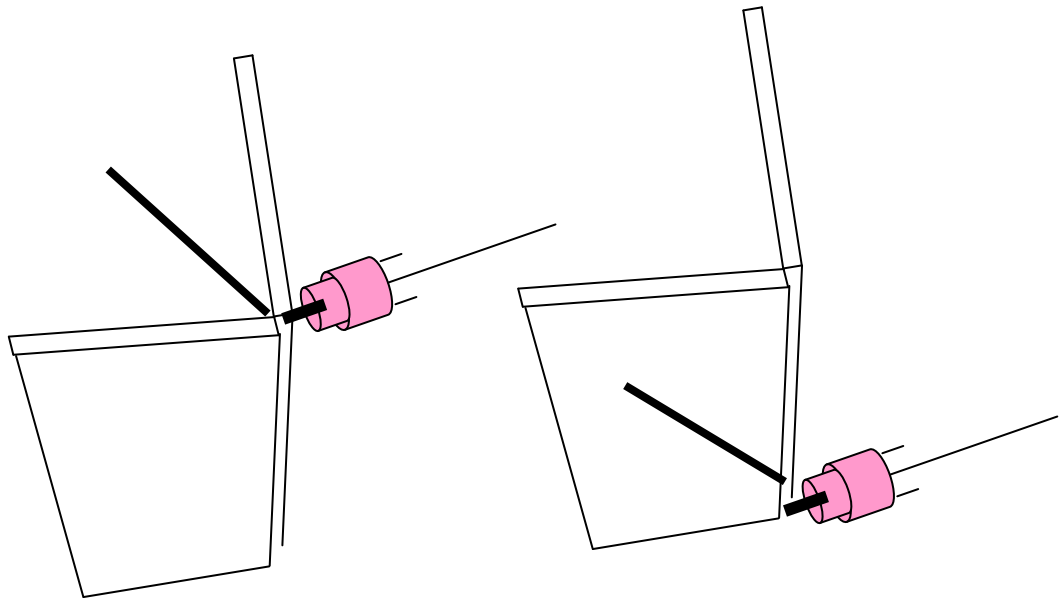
Punteado de las placas para lograr el ensamblaje a soldar.
